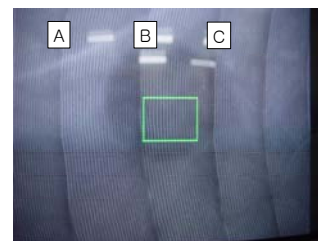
Fracture surface of the CD-R 디스크
